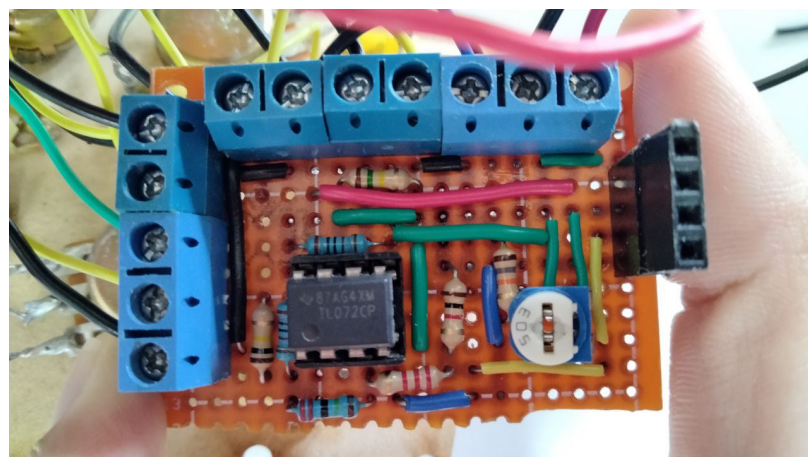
Segunda placa soldada para módulo de VCO
